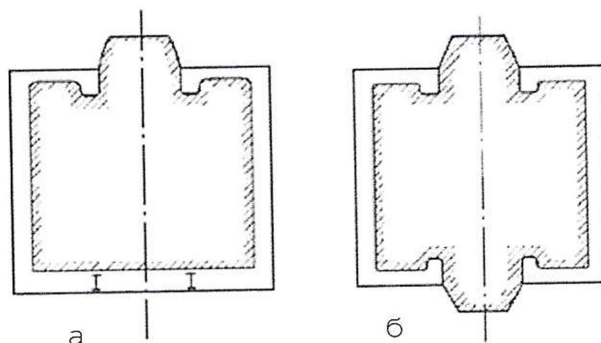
Пример устройства жеребеек и дополнительных отверстий для выхода знака стержня:
